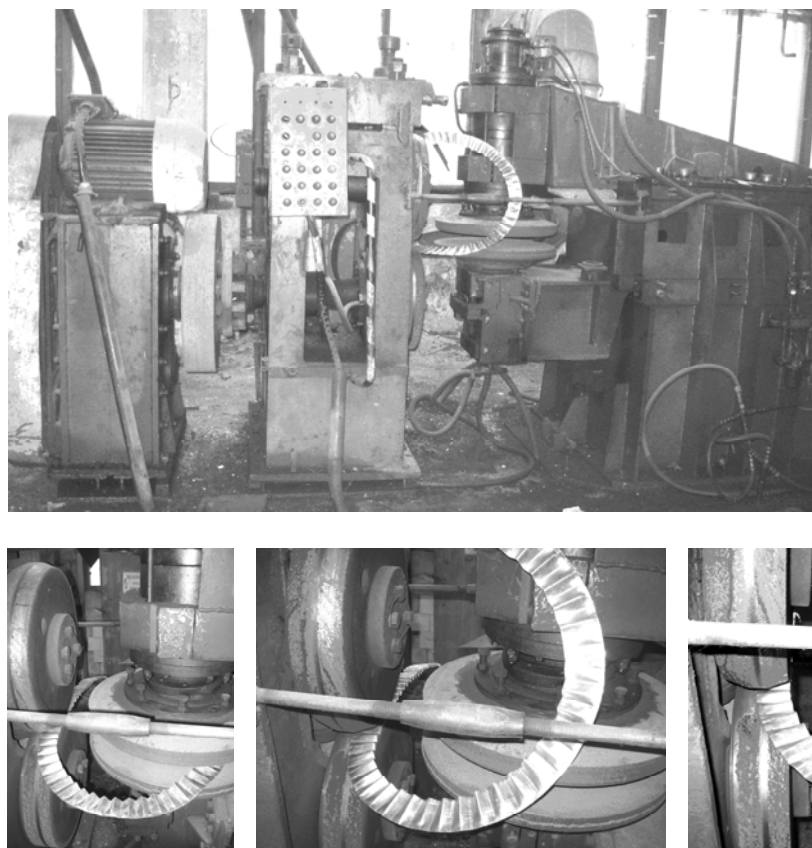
Загальний вигляд установки для виготовлення гвинтових гофрованих заготовок
